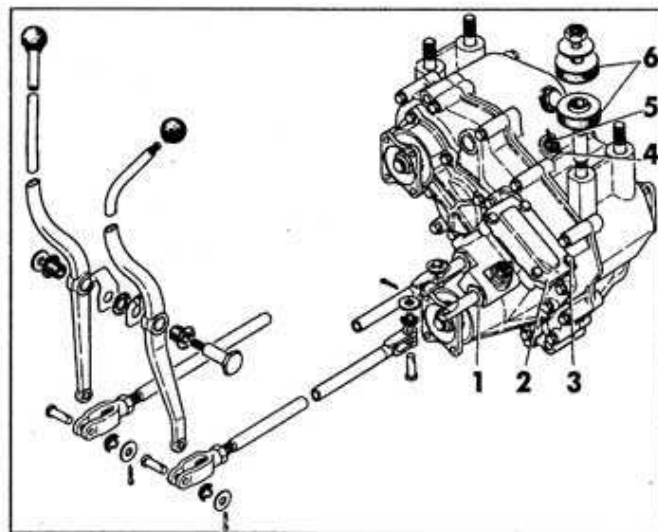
Раздаточная коробка и ее привод; 1 – гайка манжеты штока; 2 – крышка люка; 3 – болт крепления крышки люка; 4 – шплинт; 5 – ось; 6 – подушка
